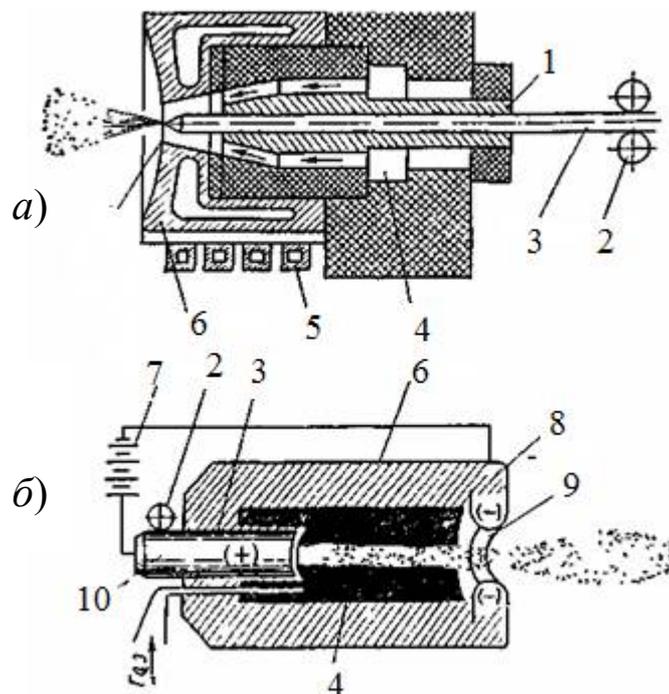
Металлизаторы: *а* – высокочастотный; *б* – плазменный; 1 – направляющая втулка; 2 – подающие ролики; 3 – электрод; 4 – воздушная камера; 5 – индуктор; 6 – корпус; 7 – источник питания; 8 – катод; 9 – сопло; 10 – анод
